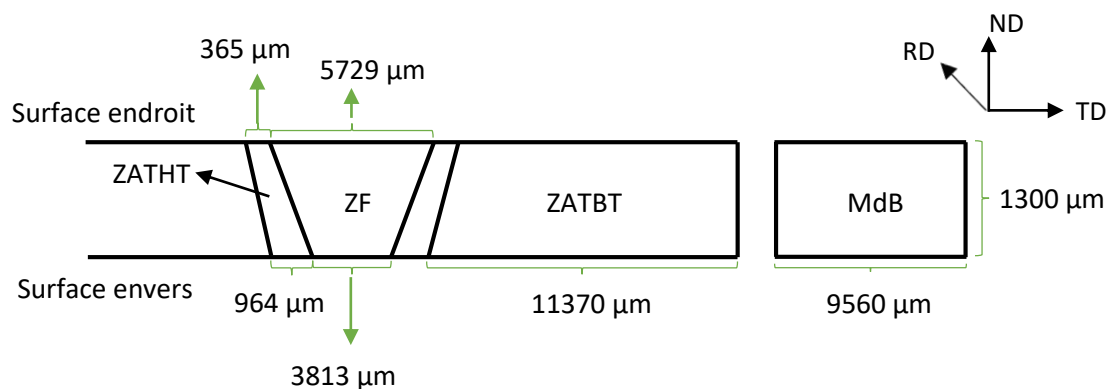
Echantillon en coupe transversale : dimensions des différentes zones qui font partie de la soudure.
